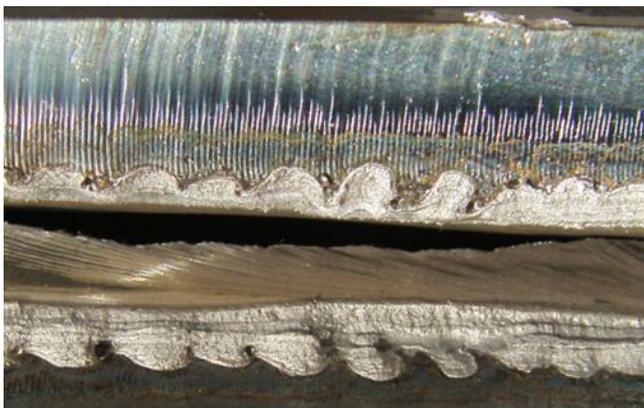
Ansicht der (eingeschliffenen) Bruchkante der Schweißung von Bild 6.
